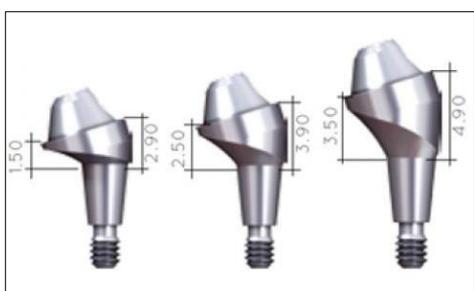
Exemplo de pilar para prótese parafusada (mini-pilar cônico angulado 17°)
